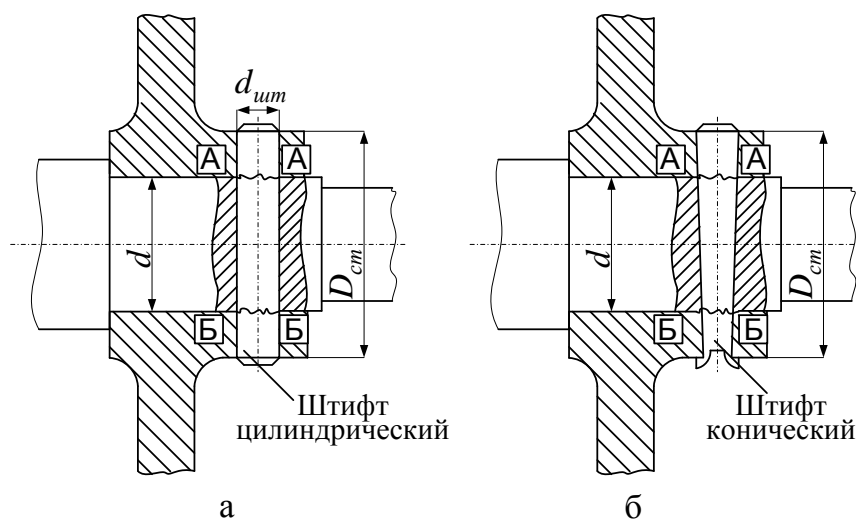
Соединение вал – ступица радиальными штифтами
